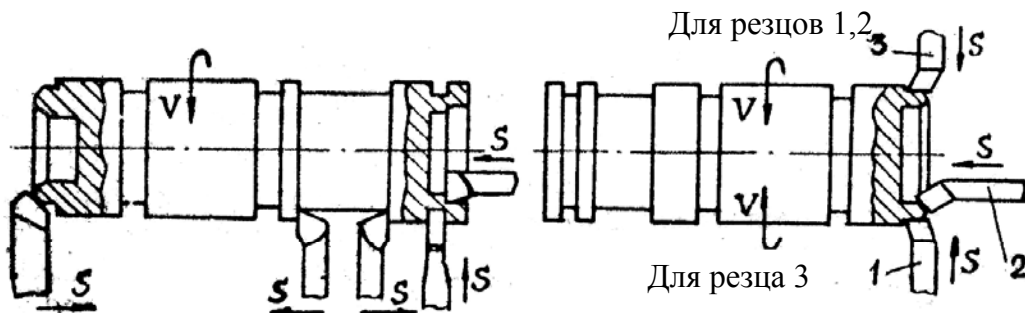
Расположение резцов относительно заготовки в приспособлении.
